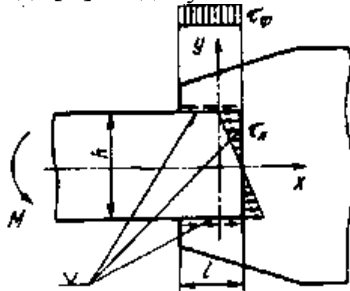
Схема к расчету нахлесточного сварного соединения, нагруженного моментом
